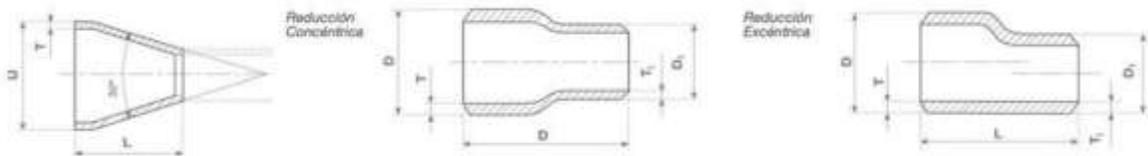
Tipos de Reductores. Fuente: Catalogo Tubos y accesorios en acero al carbono soldado y sin soldadura Normas EN (DIN) y ASTM. Tubasol S.A
